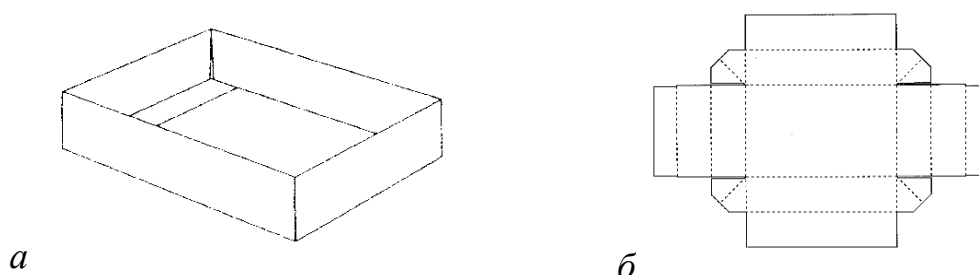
Внешний вид (а) и развертка (б) лотка с самозакрывающимися двойными стенками
